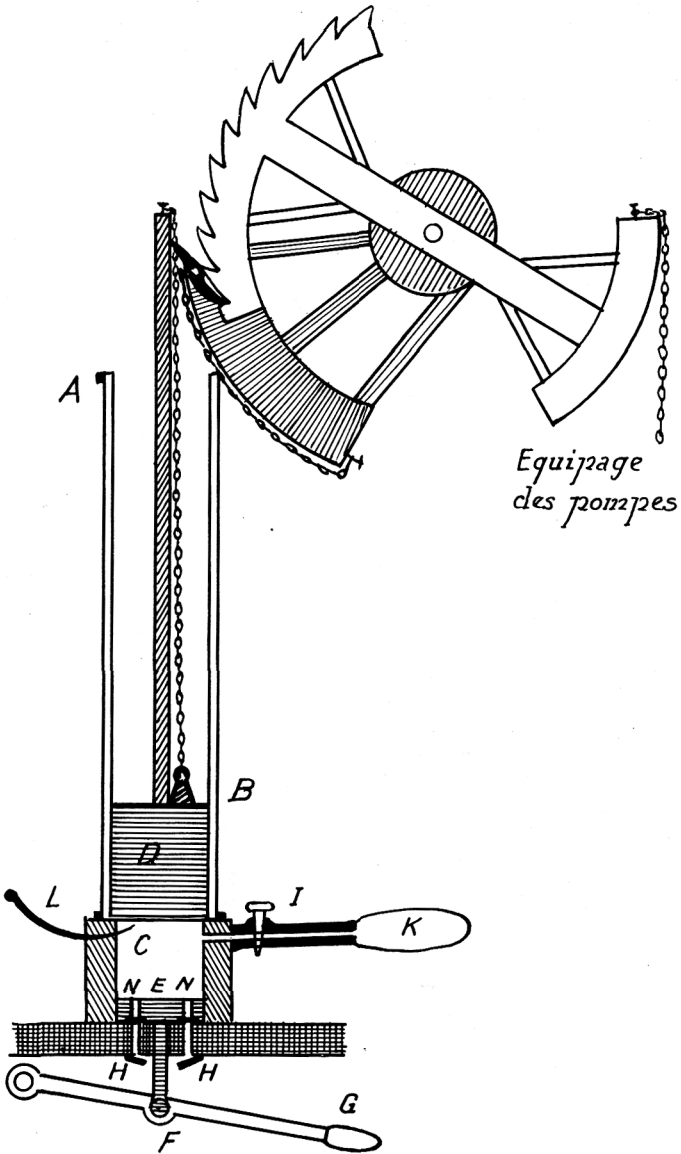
Le moteur à explosion de 1805. — AB : cylindre en section. C : boîte de métal. D : piston moteur. E : piston de charge. F : branche de manèment. G : levier. H : ouvertures avec soupapes. J : tuyau. K : mesureur. L : électrode en métal. N : ouvertures.
